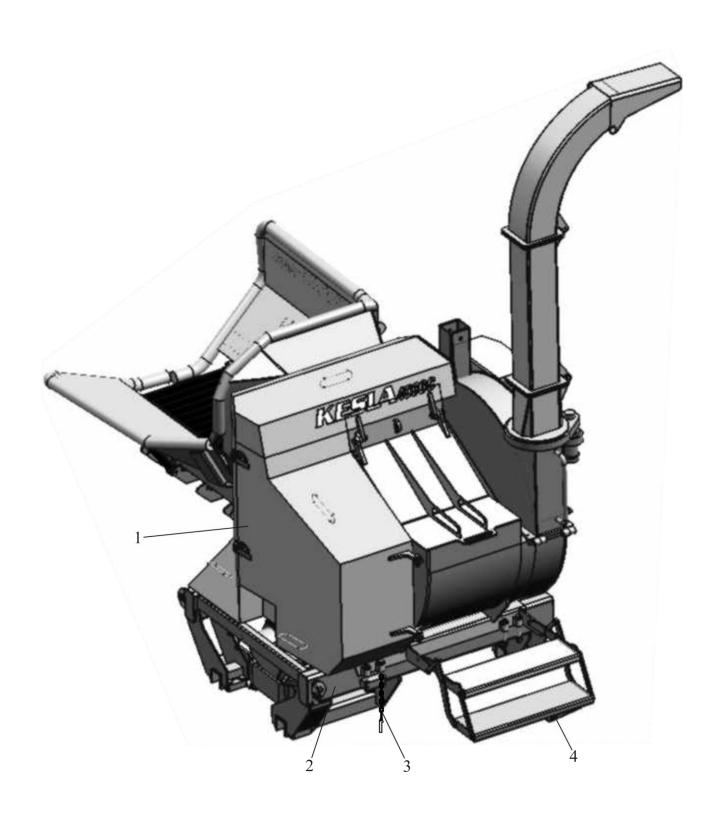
(лист 1 из 2) – Агрегат дробильный
